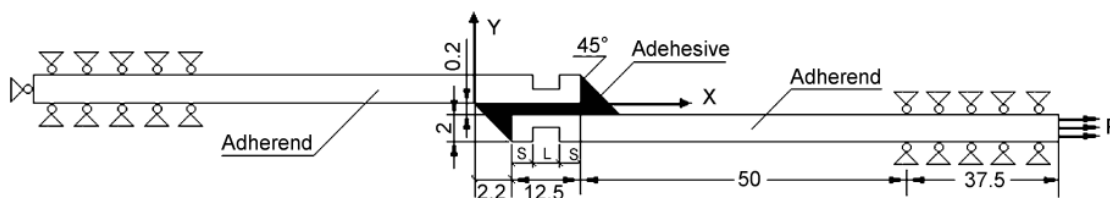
Geometria da junta ensaiada, carga e condições fronteira aplicadas [47]
